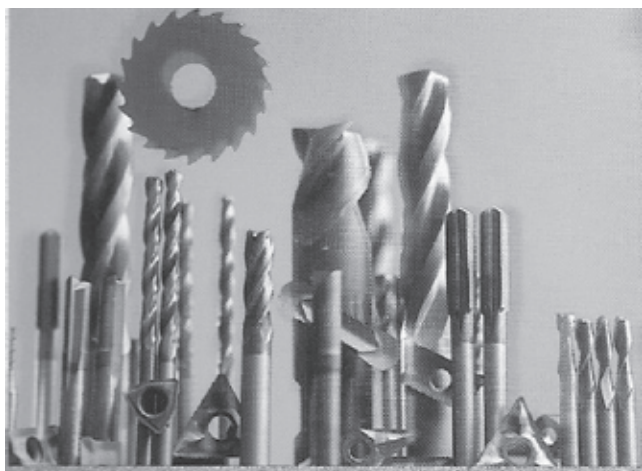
Recubrimientos de CrN depositados sobre herramientas de corte – maquinado y moldes de inyección
